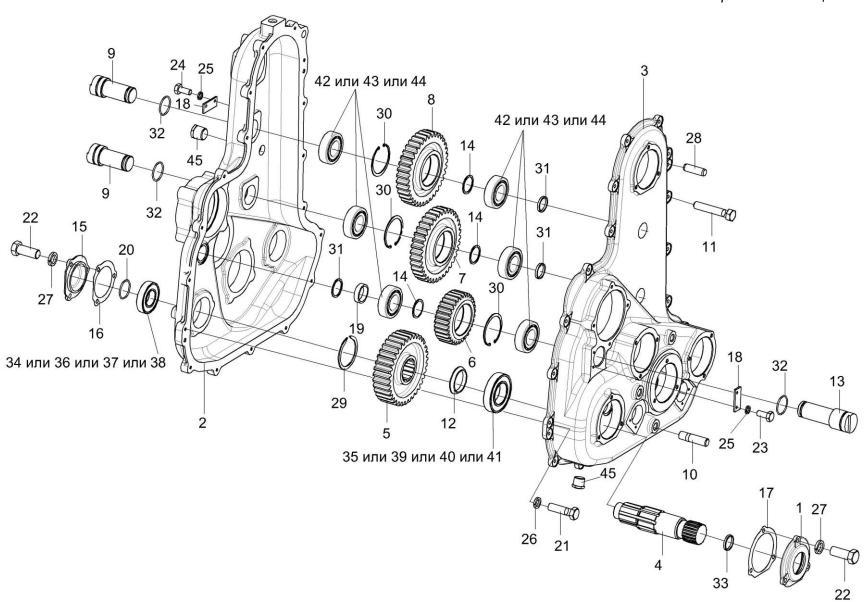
Редуктор КВК 0114100 (лист 2)
